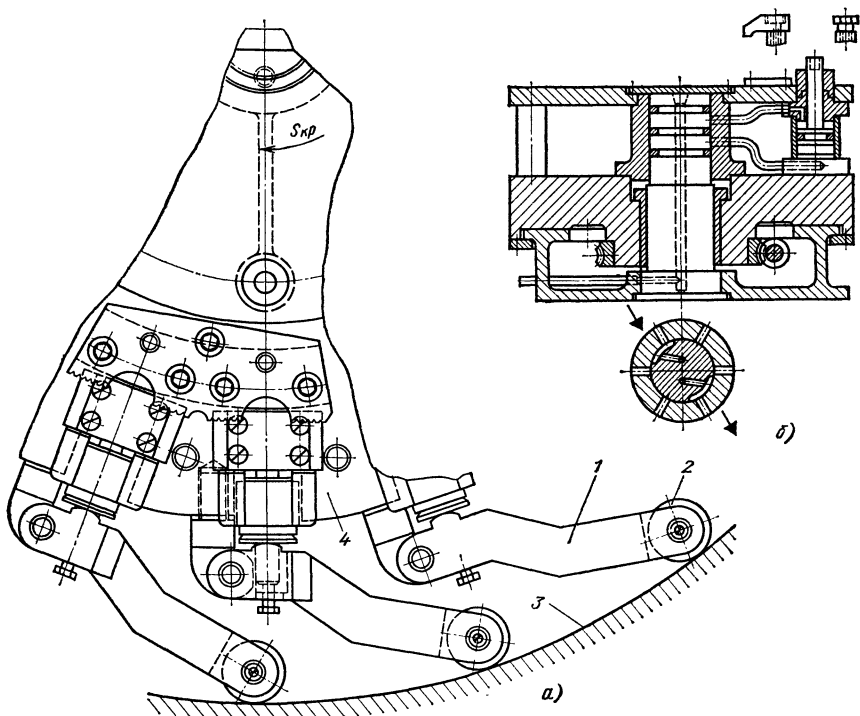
Зажимной механизм приспособлений к станкам непрерывного действия
